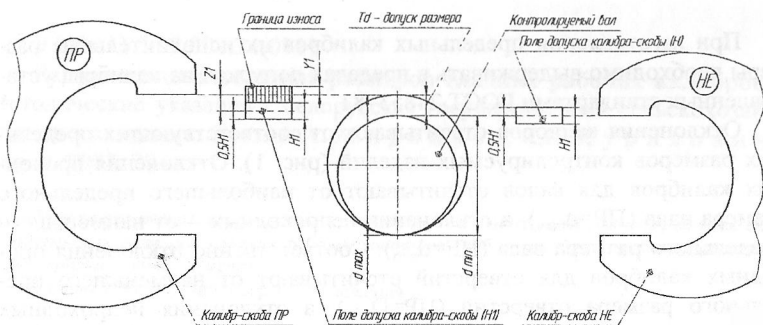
Схема расположения полей допусков калибров-скоб для контроля валов $D < 180$ мм, изготовленных по 6,7 и 8-му квалитетам точности: d_{\max} – наибольший предельный размер вала, мм; d_{\min} – наименьший предельный размер вала, мм; Td – допуск размера вала, мкм; H_1 – допуск на изготовление калибра-скобы, мкм; Z_1 – координата середины поля допуска на изготовление проходного калибра-скобы, мкм; Y_1 – допустимый выход размера изношенного проходного калибра-скобы за границу поля допуска размера, мкм.
